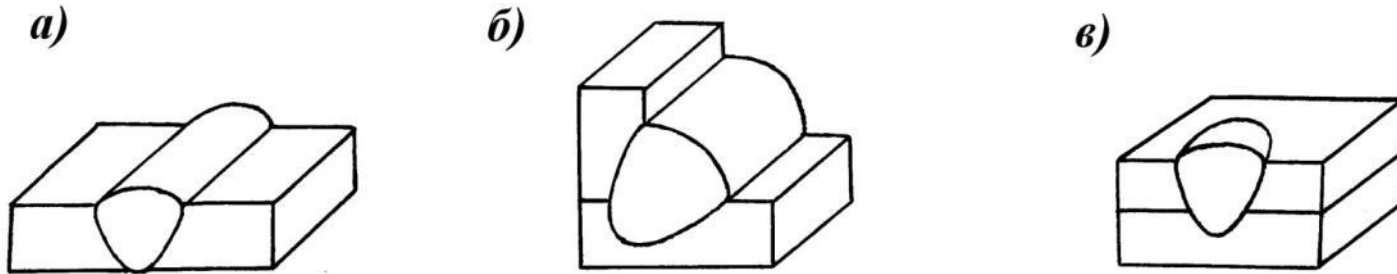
Типы сварных швов по ГОСТ 2601-84:
